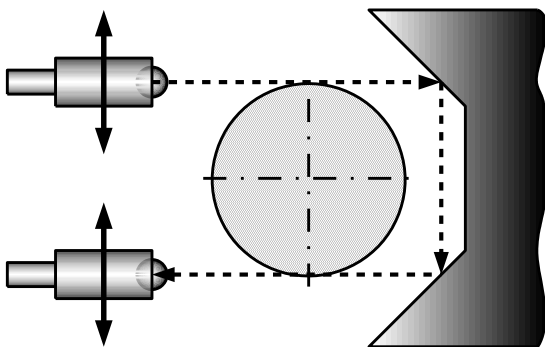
Тіньовий двобічний лазерний вимірювальний пристрій
